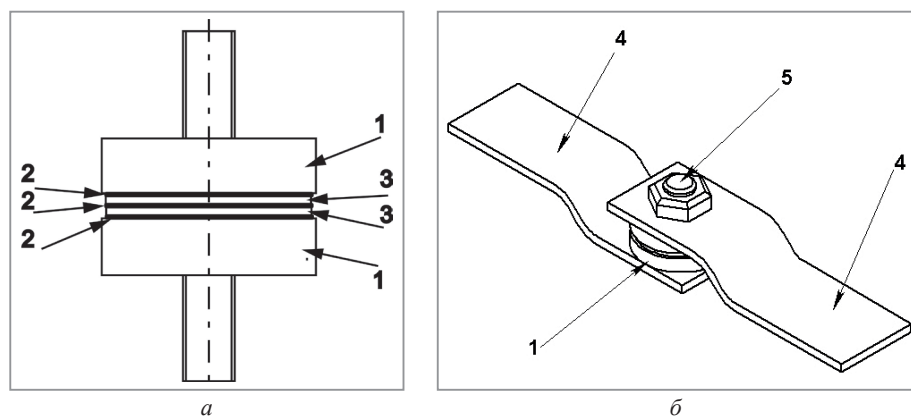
Образец и приспособление для проведения механических испытаний многомерного композиционного соединения:
